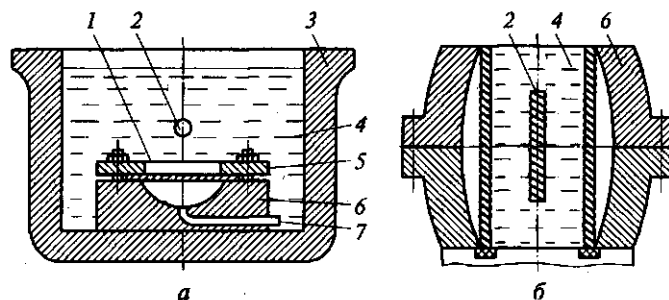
Схема штамповки взрывом деталей из плоской (а) и трубной (б) заготовки в стационарном бассейне:
